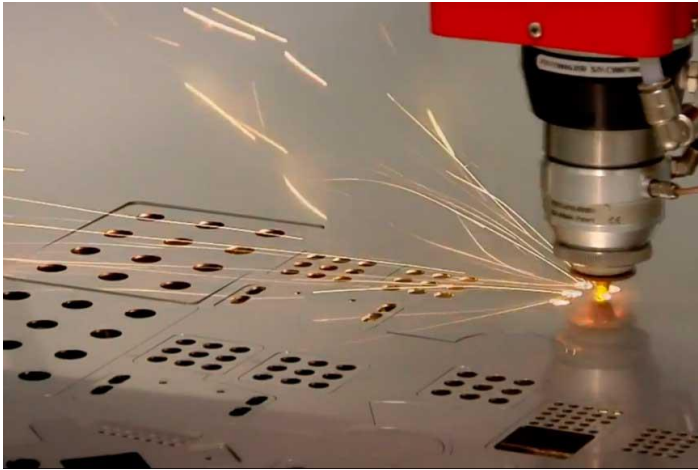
Приклад лазерного свердління металу [38]
